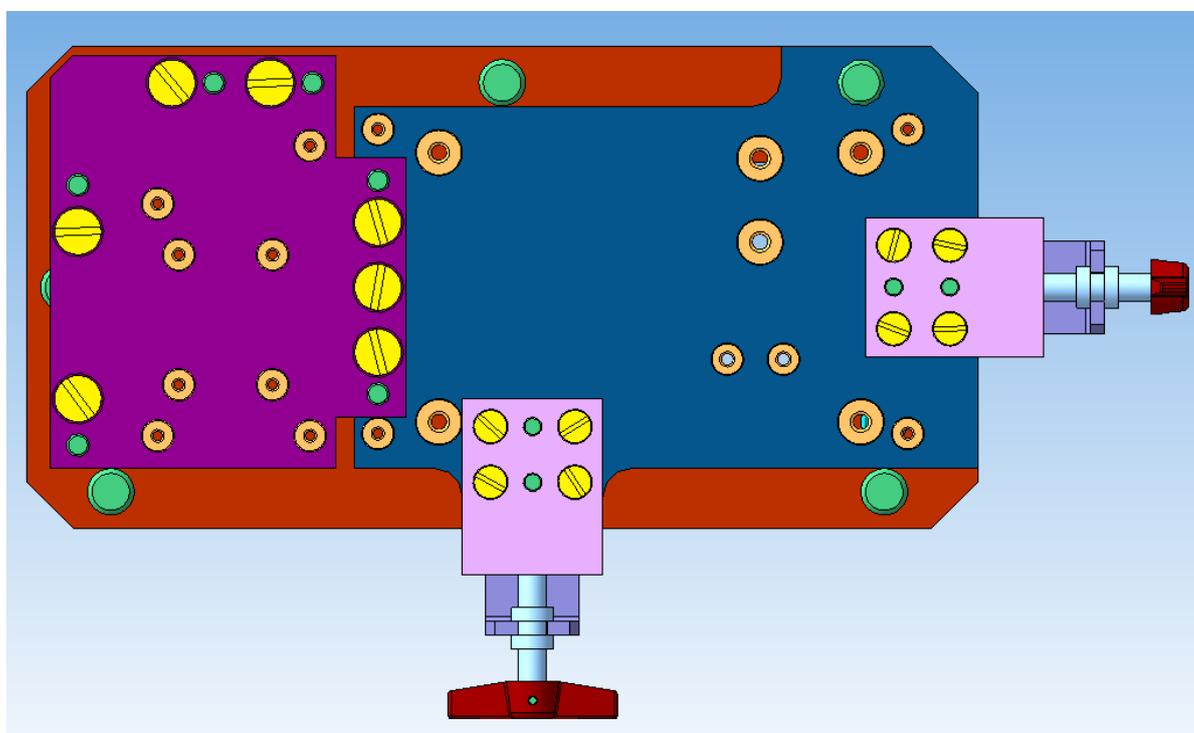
Трехмерная модель зажимного приспособления (вид сверху)
